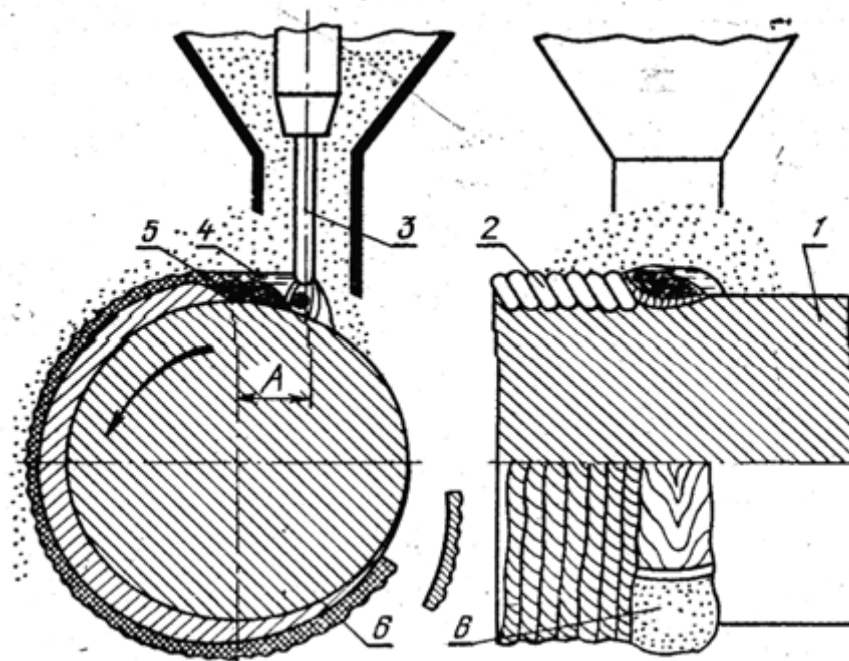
Наплавлювання під шаром флюсу: 1 – деталь; 2 – наплавлений шар; 3 – електрод; 4 – розплавлений флюс; 5 – ванна розплавленого металу; 6 – шлакова кірка; А – зміщення електрода із zenіту
